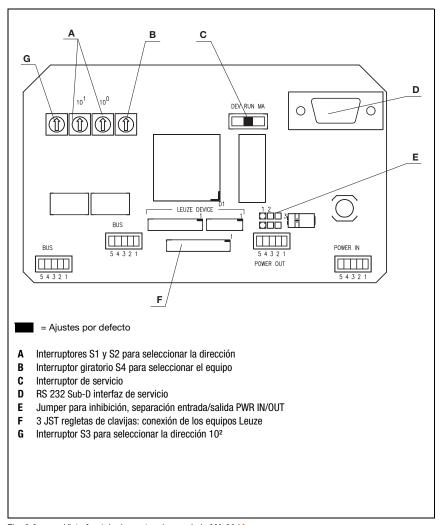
Vista frontal: elementos de uso de la MA 204i
